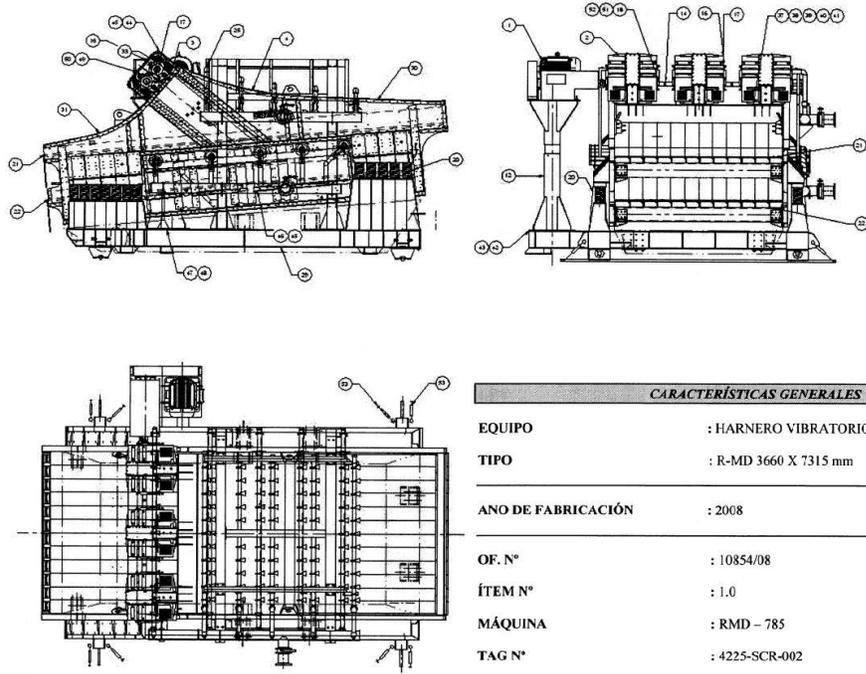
plano general del Harnero vibratorio, Planta Confluencia
